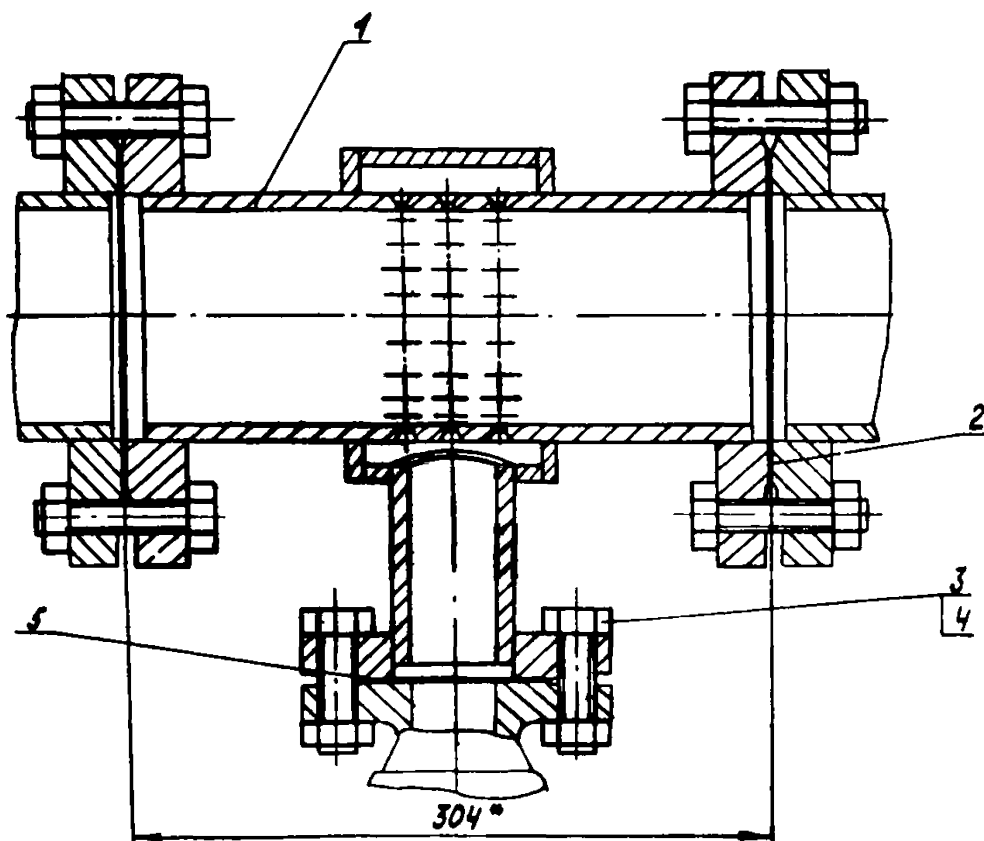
Распределительная головка для ввода ингибитора (сборочный чертеж):
